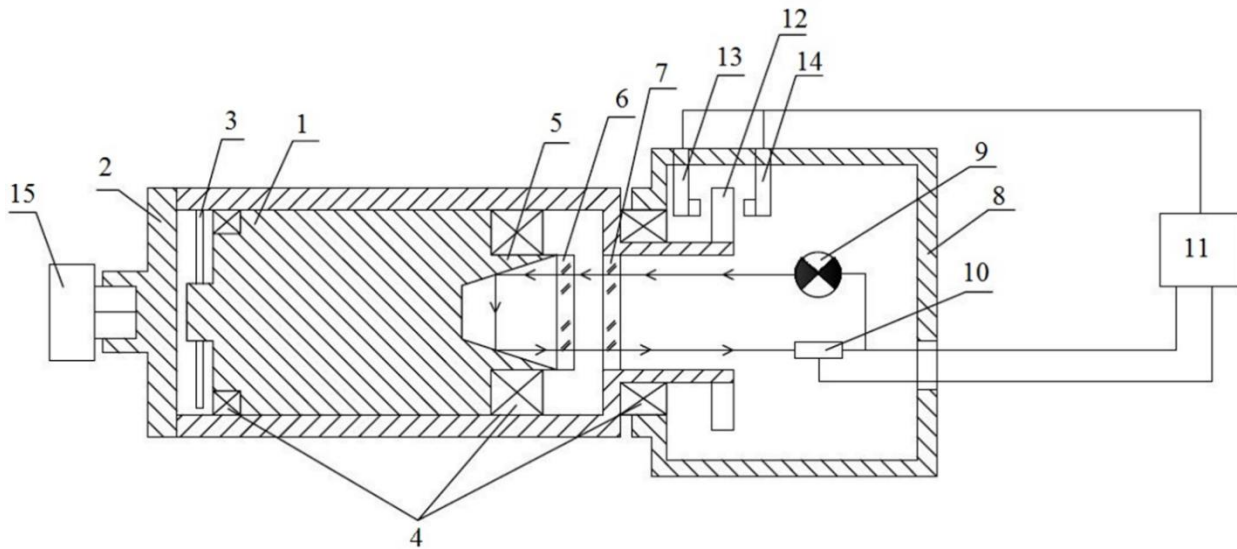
Усовершенствованное устройство определения угловой скорости вращения коленчатого вала двигателя. [38]
